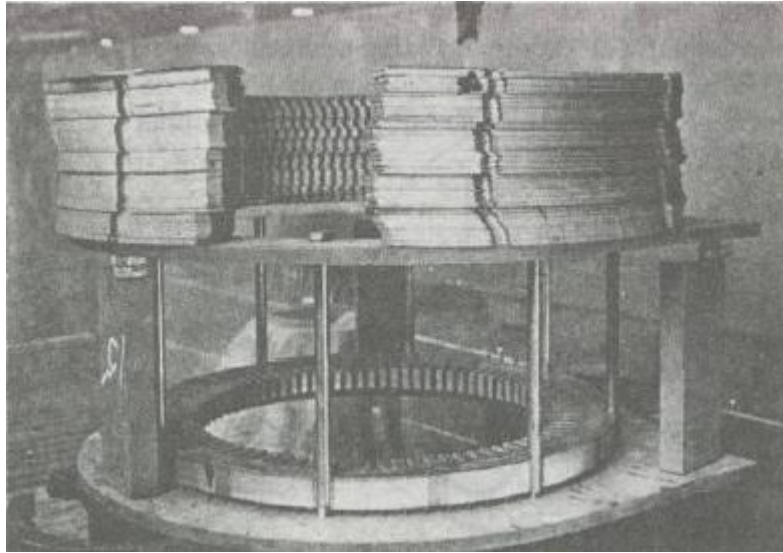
Núcleo do estator de um motor de corrente alternada, parcialmente montado
